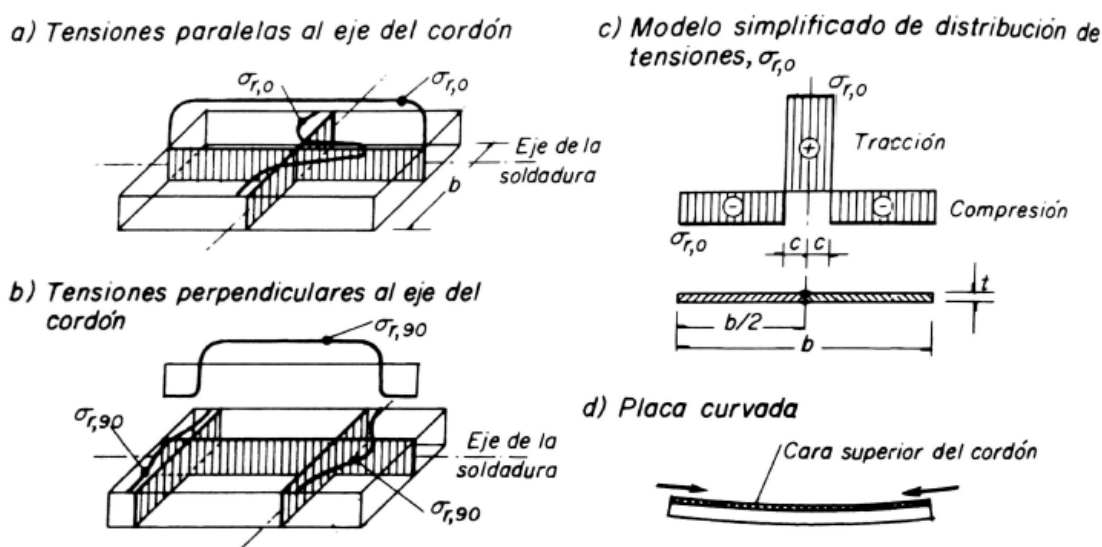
Tensiones residuales de una soldadura a tope.
